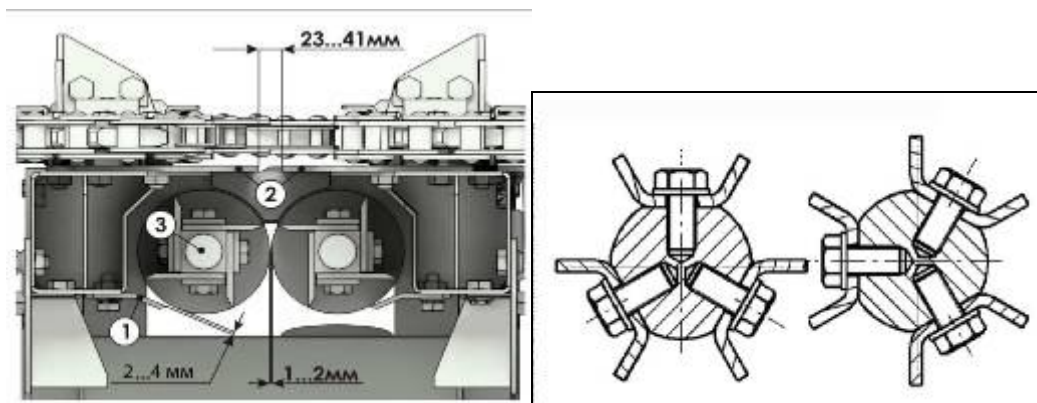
Вальцы серийного приспособления (слева) и вальцы жатки RSM MS-870-49 с шестью съёмными перекрывающимися лопастями (справа)
